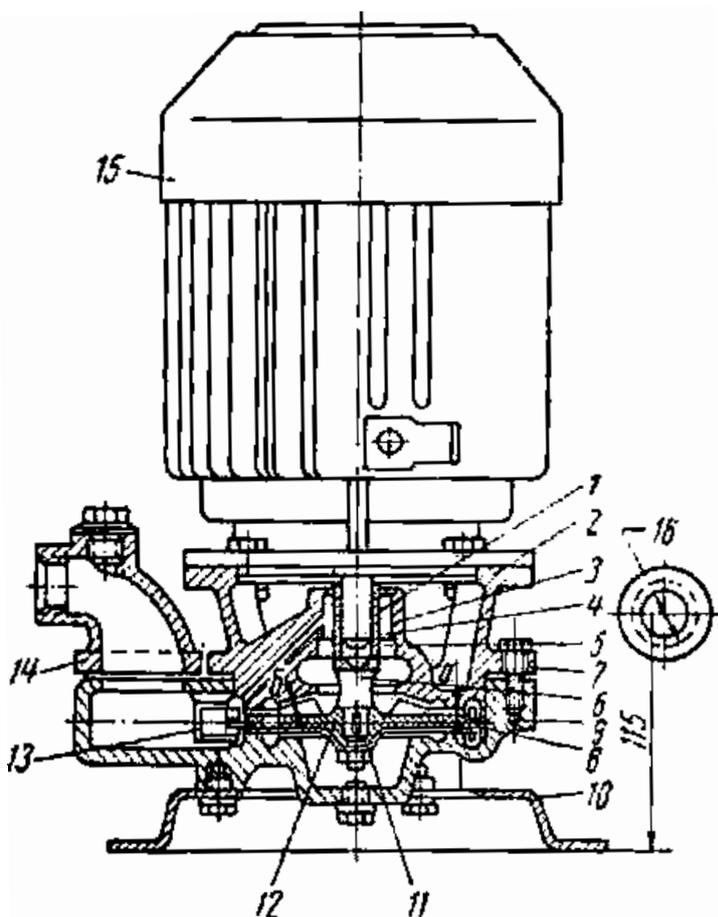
Электронасос 1СЦВ-1.5М: 1 - манжетное кольцо; 2 — фонарь; 3 — манжета; 4 — шайба; 5—гайка специальная; 6 — удлинитель вала; 7— прокладка; 8 — рабочее колесо; 9 — корпус; 10 — полетовка; 11 — шайба-замок; 12— шайба регулировочная; 13 — воздухоотвод; II — колпак; 15 — электродвигатель АОЛБ32-4; 16 — всасывающий патрубок
